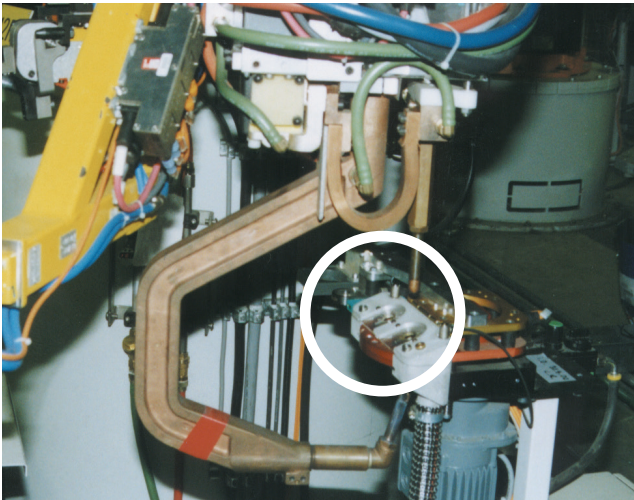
Mess- und Bearbeitungsstation für Schweißzangen-Elektroden
